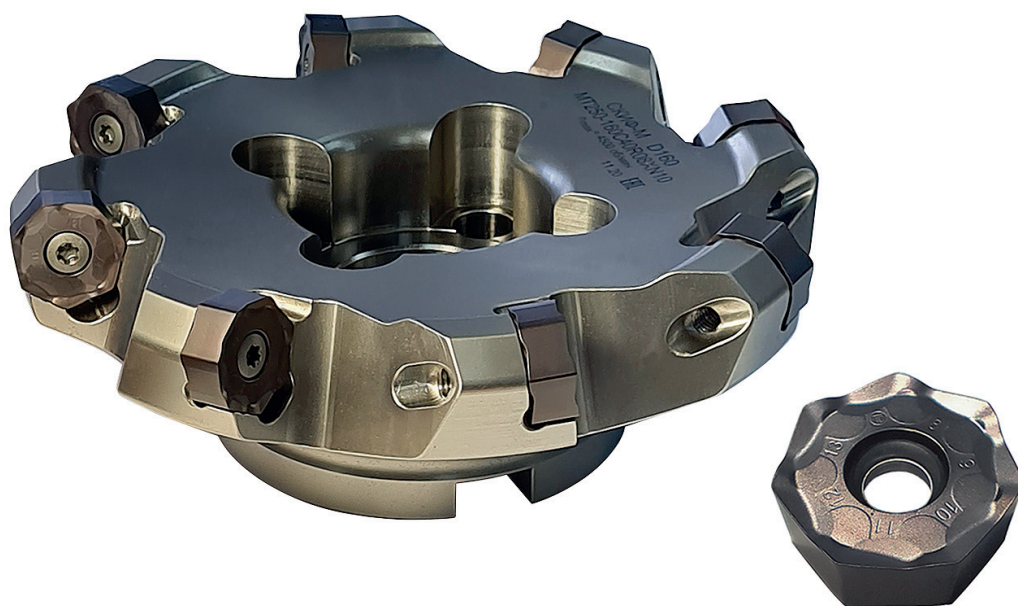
Торцовая фреза с двухсторонними семигранными пластинами
